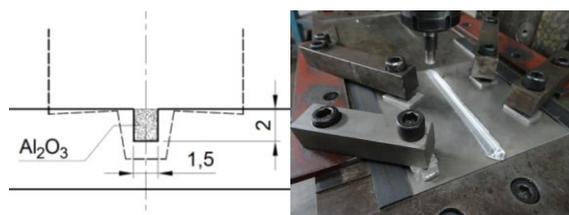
(izq.) Geometría de ranura y herramienta para FSP; (der.) Montaje experimental para FSP empleado.
